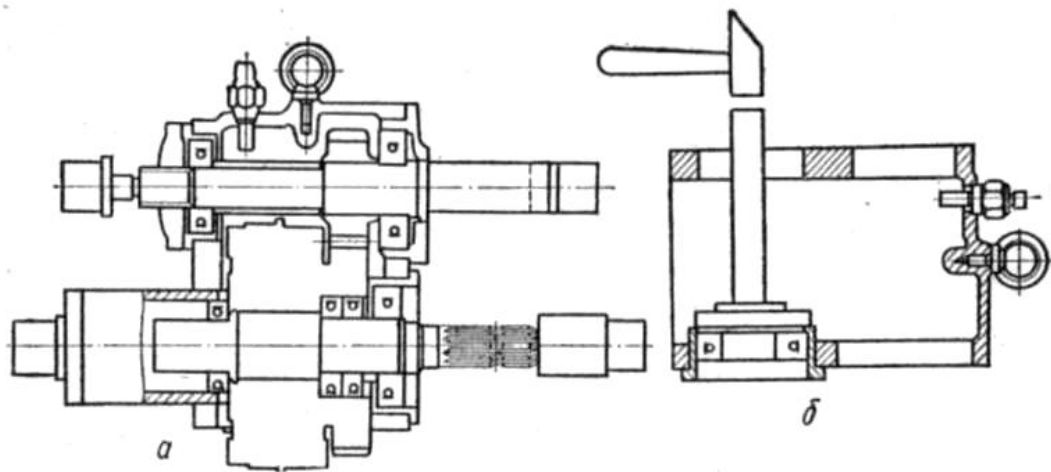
Схема розміщення пристроїв стенда під час розбирання редуктора вала відбору потужності:
